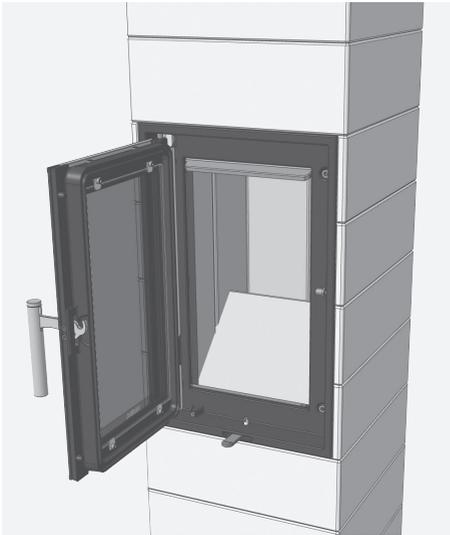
Dépose de la sole foyer de la chambre de combustion
